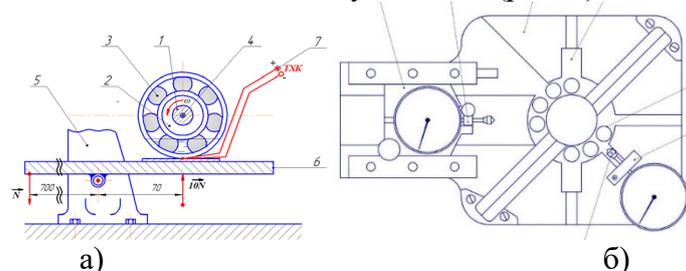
Схема опытной установки (а): 1 - вал электродвигателя; 2 - переходная втулка подшипника; 3 - подшипник; 4 - гайка фиксирующая подшипник; 5 - кронштейн для крепления нагружающей балки; 6 - нагружающая балка; 7 - термопара цифрового прибора ТМ-902С; прибор КИ-1223 (б) для контроля радиального зазора, укомплектованный микрокатерными измерительными головками (1 мкм).
